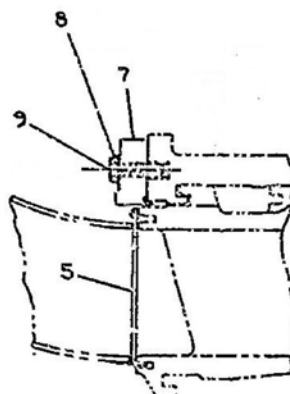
LTPI-15 - Dispositivo di sollevamento per la rimozione dell'involucro della camera di combustione
